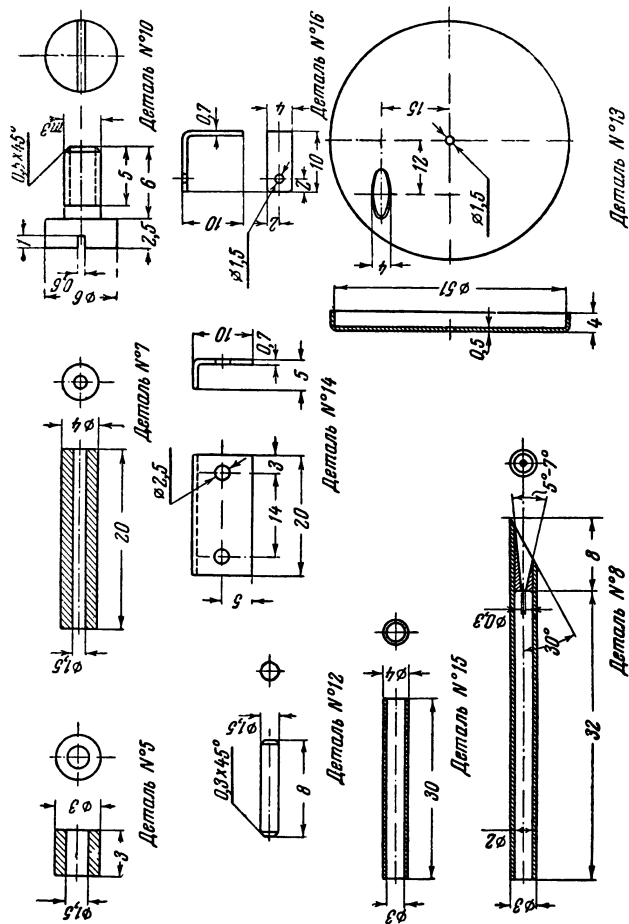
Чертежи деталей паровой турбины: деталь № 5 — ограничительная втулка; деталь № 7 — вал диска; деталь № 8 — сопло; деталь № 10 — винт; деталь № 12 — ось вала диска; деталь № 13 — крышка корпуса; деталь № 14 — скобка крепления паровой турбины; деталь № 15 — пароводные трубки, деталь № 16 — пьедестал
